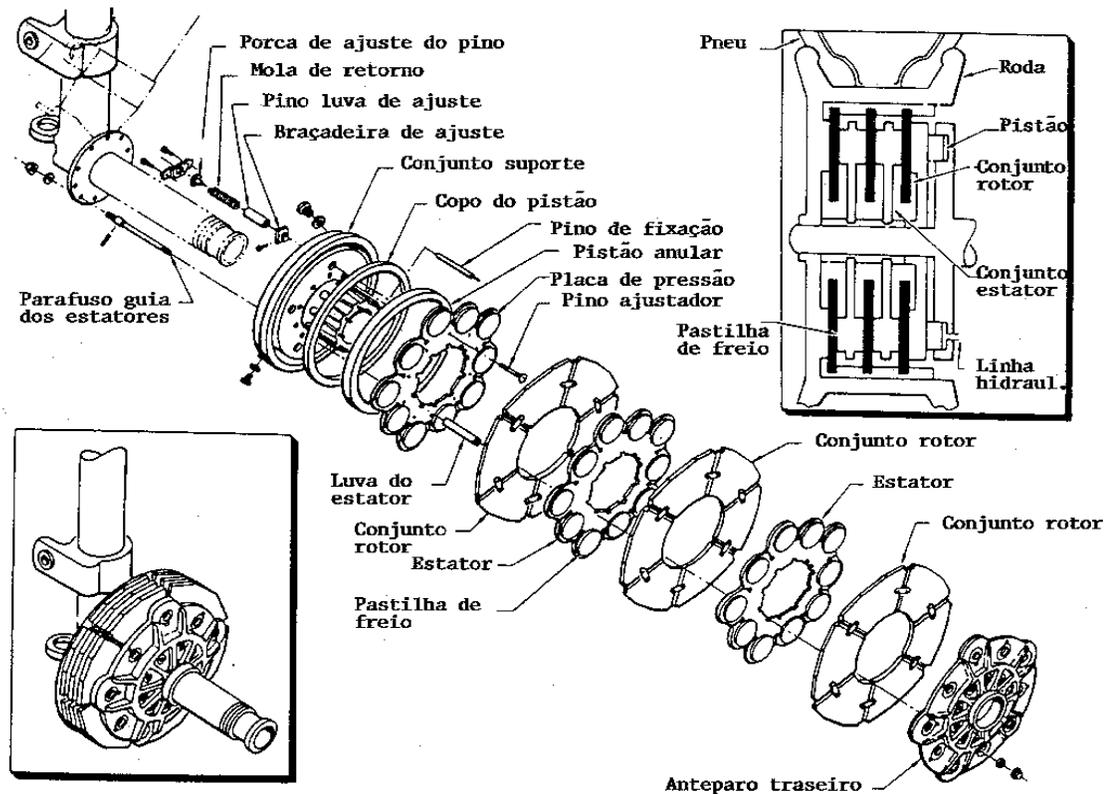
Unidades de um conjunto de freio de rotor segmentado
